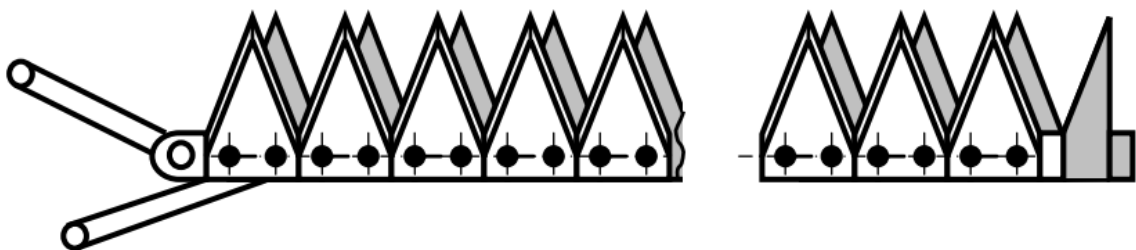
Схема сегментного двухножевого режущего аппарата
